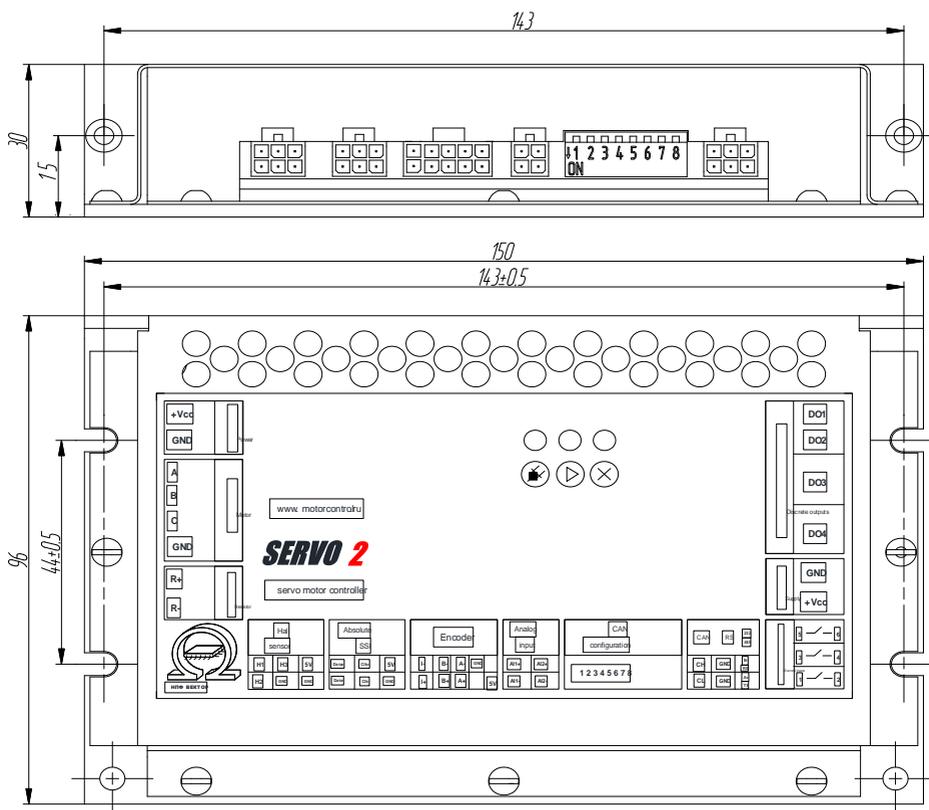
Габаритные и присоединительные размеры (* размеры для справок)
